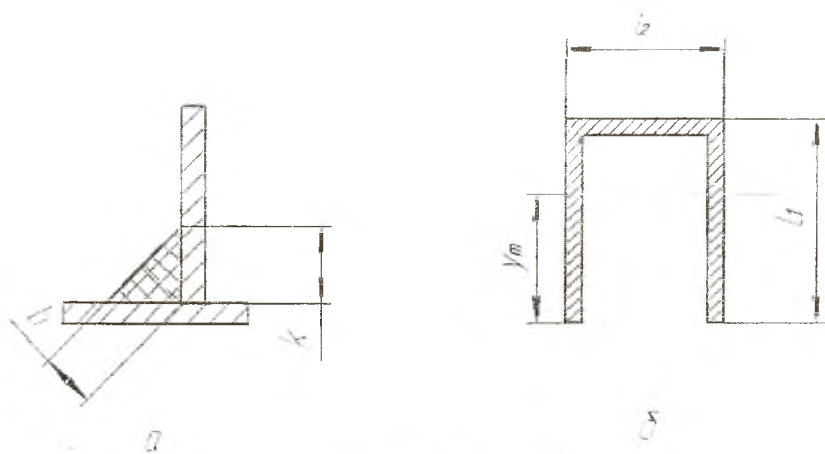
Угловой сварной шов (а) и расположение шва по контуру опоры (б)
